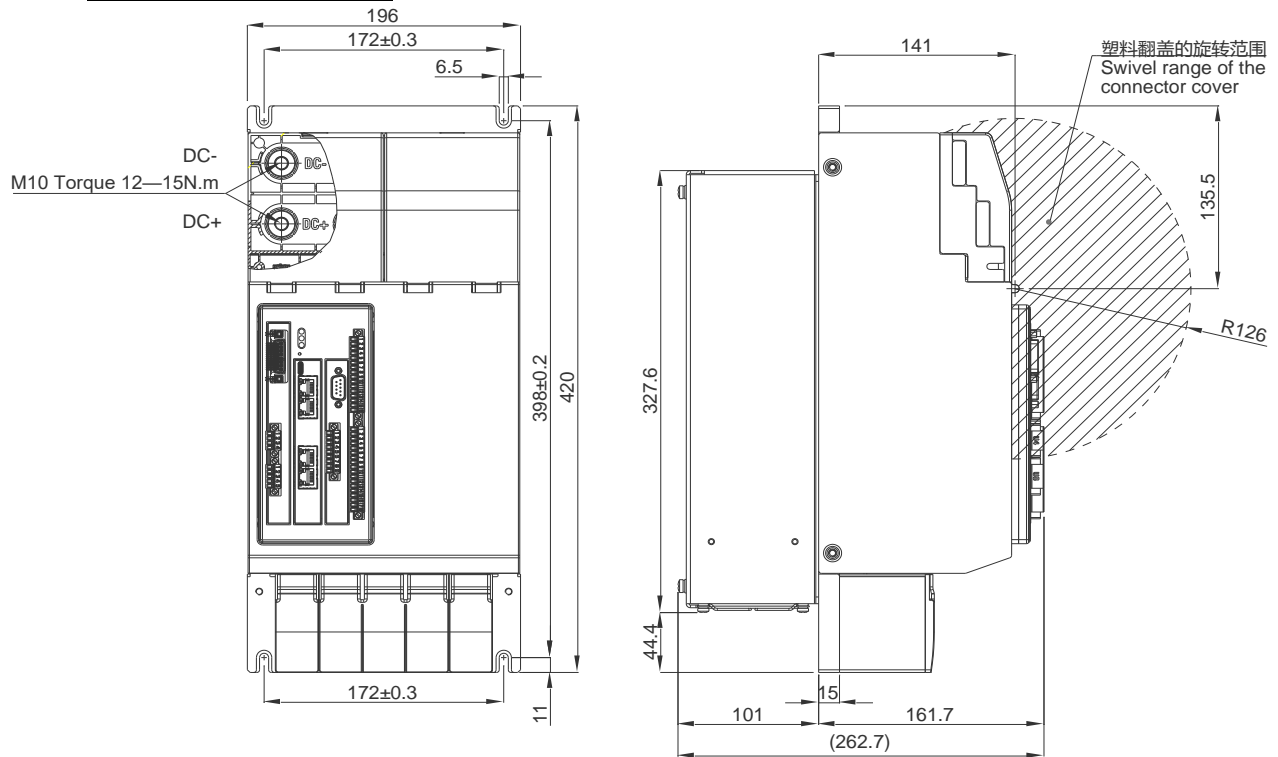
AxN-PS.080.4 穿墙安装 Feed-through mounting
